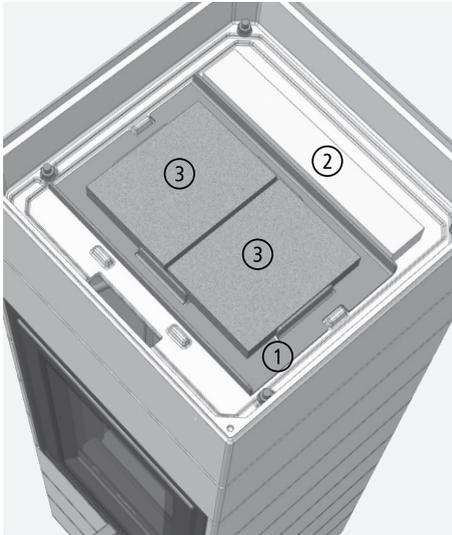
Positionnement des plaques du catalyseur du CORNA tec, vue de dessus, couvercle ôté
